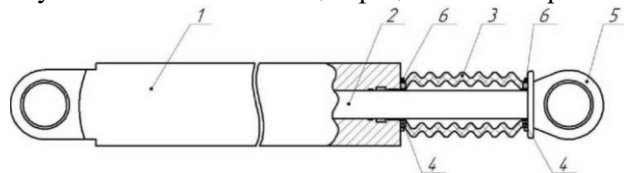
Схема устройства: 1 – корпус гидроцилиндра; 2 – шток гидроцилиндра; 3 – гофрированная труба; 4 – кольцевые магниты; 5 – ухо штока гидроцилиндра; 6 – упорный выступ.
